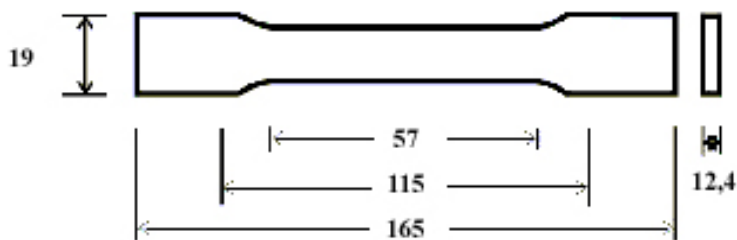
Dimensões, em mm, do corpo de prova de tração
